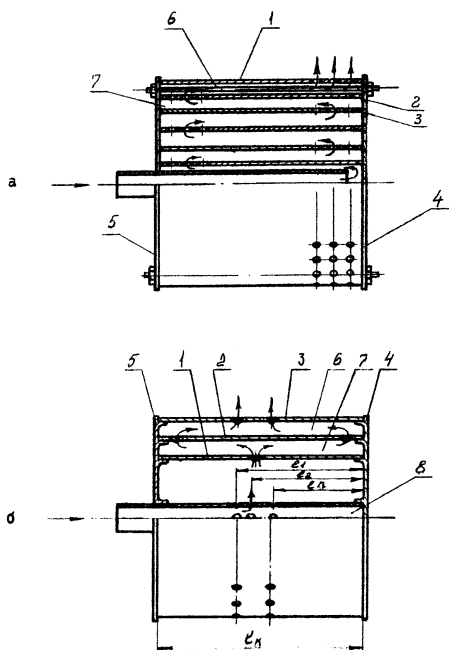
Реактивные камерные глушители шума: а - ;
